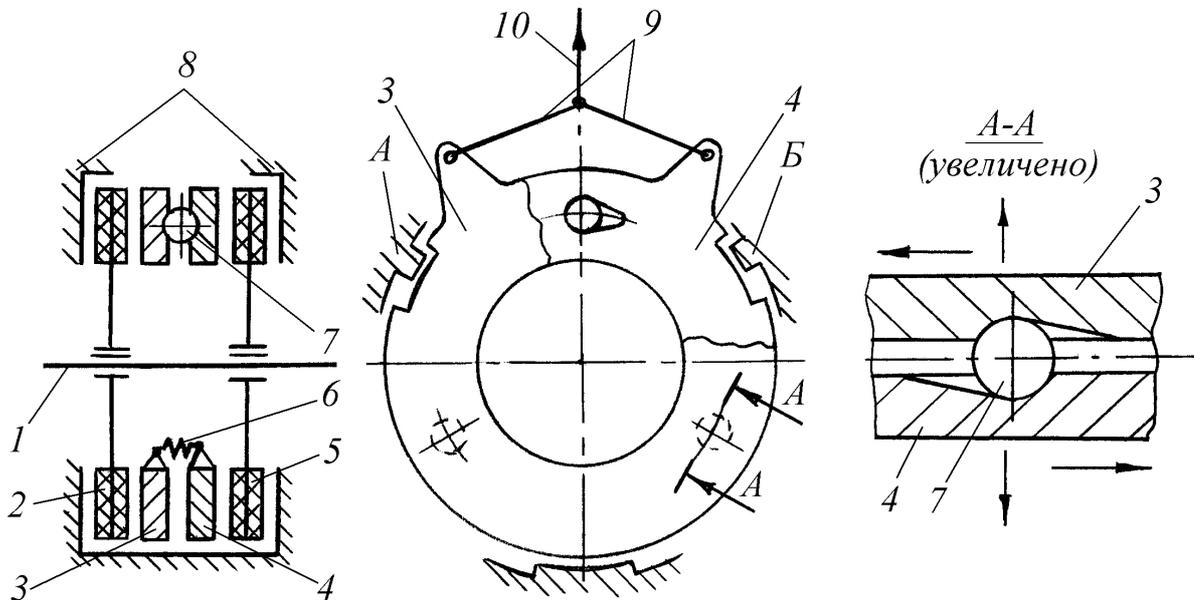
Схема закрытого дискового тормоза с сервоусилением
